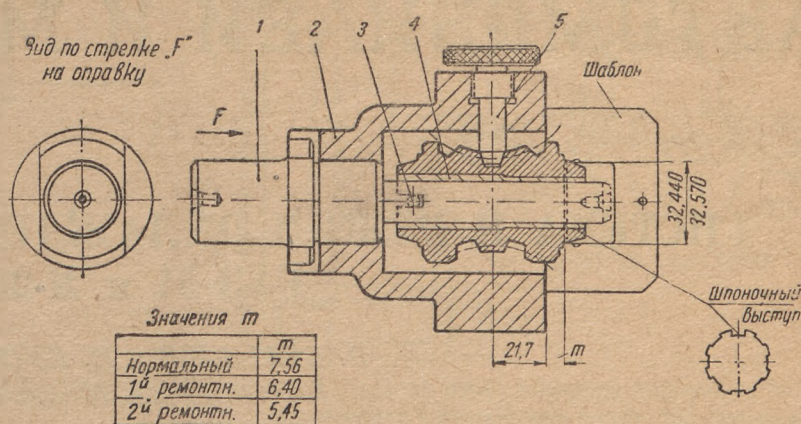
Приспособление для обточки конуса червяка на токарном станке: 1 — оправка; 2 — корпус; 3 — штифт; 4 — втулка; 5 — фиксатор.
